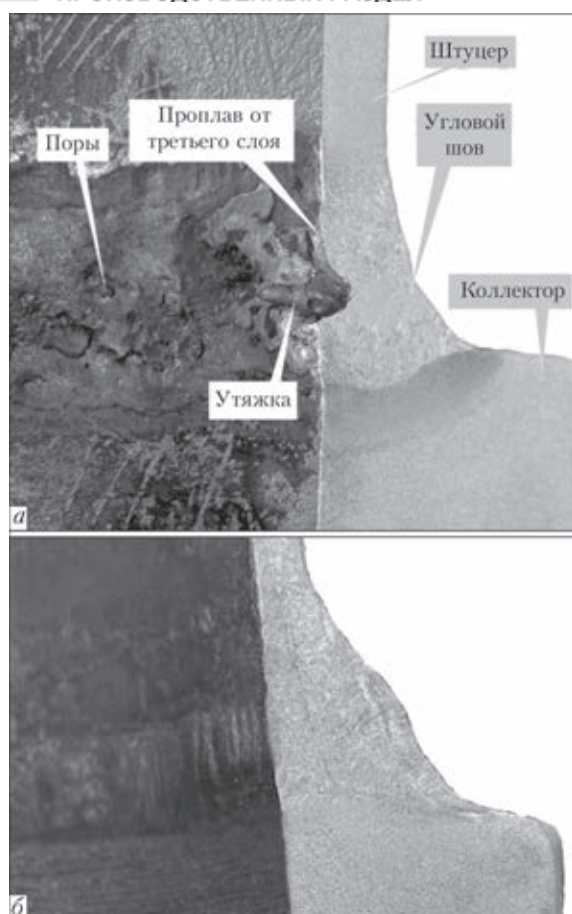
Угловые сварные соединения штуцера с коллектором: *а* — поперечное сечение соединения с дефектами в корневом валике, выполненного без поддува аргона; *б* — поперечное сечение соединения, выполненного с поддувом аргона
